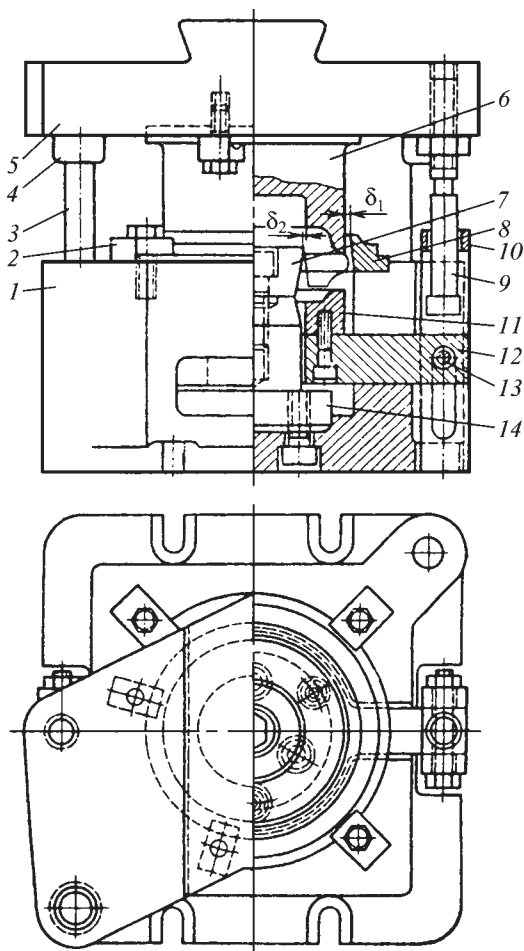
Совмещенный штамп для обрезки облоя и пробивки перемычек:
